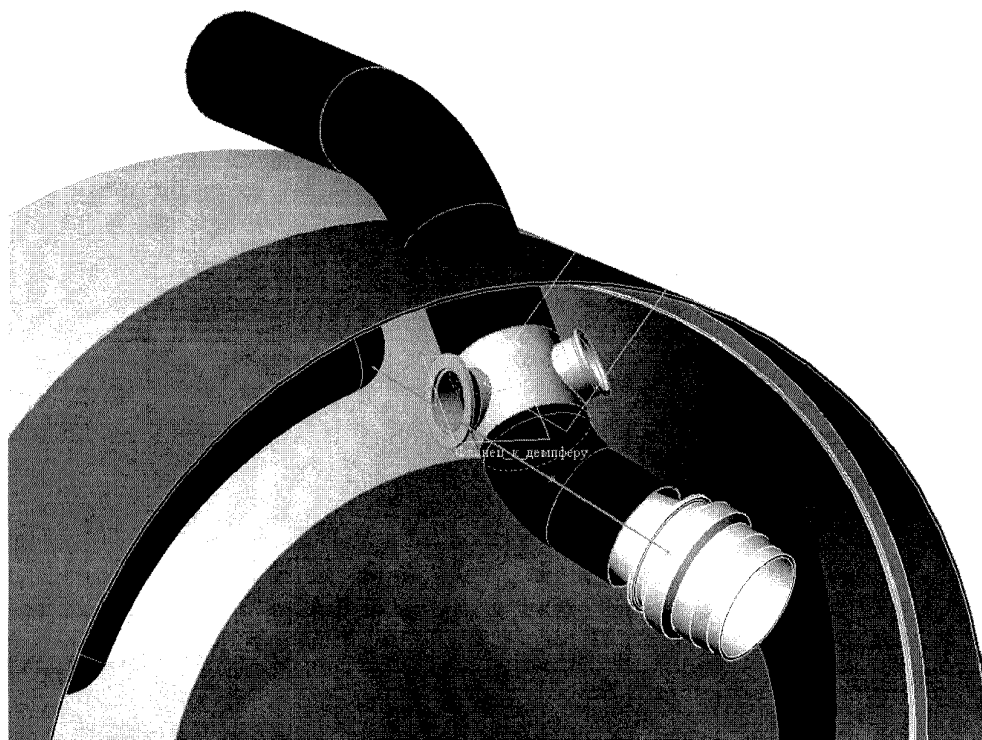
Использование фасонного элемента в трубопроводе УРМ “Ангара”
